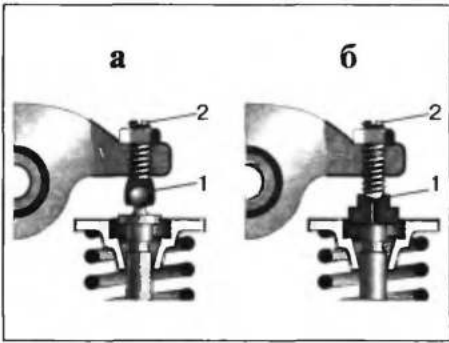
Шарнирные опоры наконечника коромысел: а — шарнир на регулировочном винте; б — шарнир, образованный соединением сферического наконечника винта со сферической впадиной толкателя; 1 — толкатель; 2 — винт
